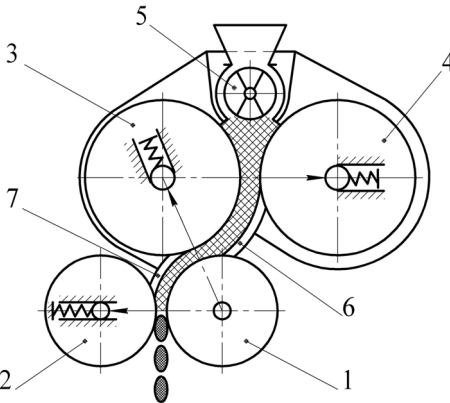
Схема валкового пресса с трехстадийным прессованием.
